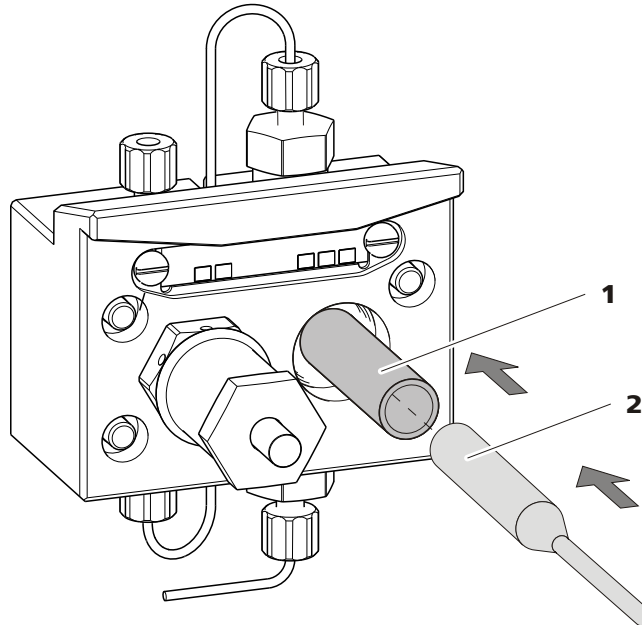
Kolbendichtung in Pumpenkopf einsetzen
